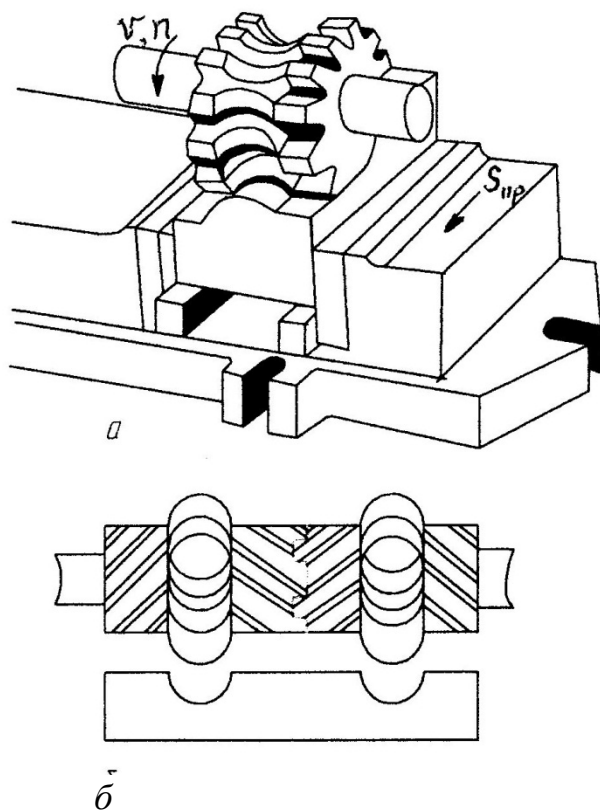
Фрезерование фасонных поверхностей фасонными фрезами
